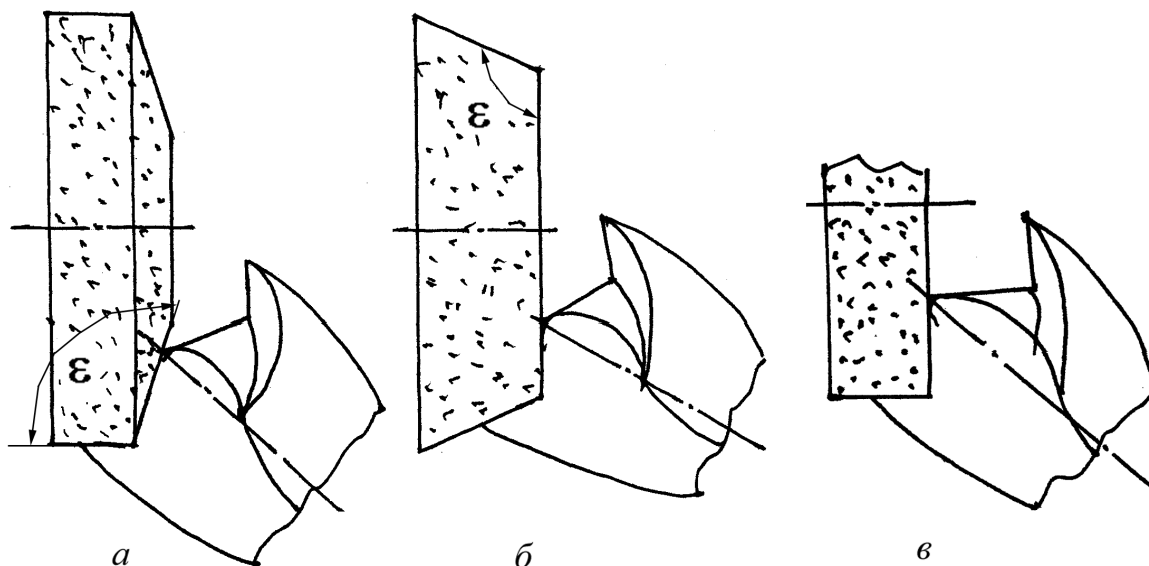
Способы заточки сверл с подрезающими режущими кромками:
